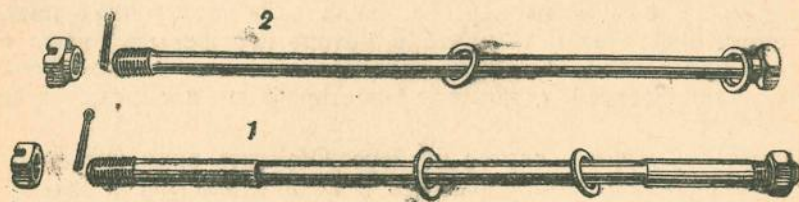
Стяжные шпильки крепления подвесок коленчатого вала.
